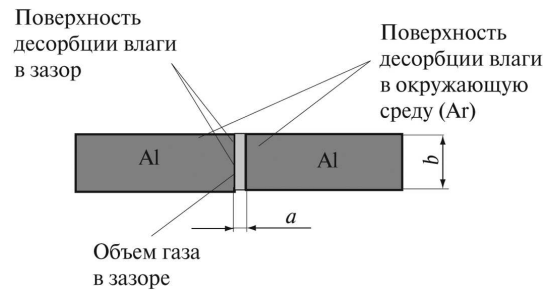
Схема выделения влаги с поверхностей свариваемых деталей при нагреве в процессе сварки:
